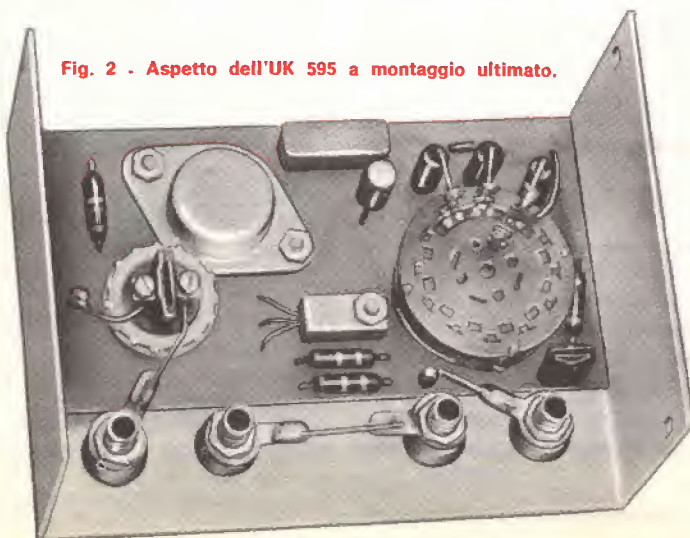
Aspetto dell'UK 595 a montaggio ultimato.
